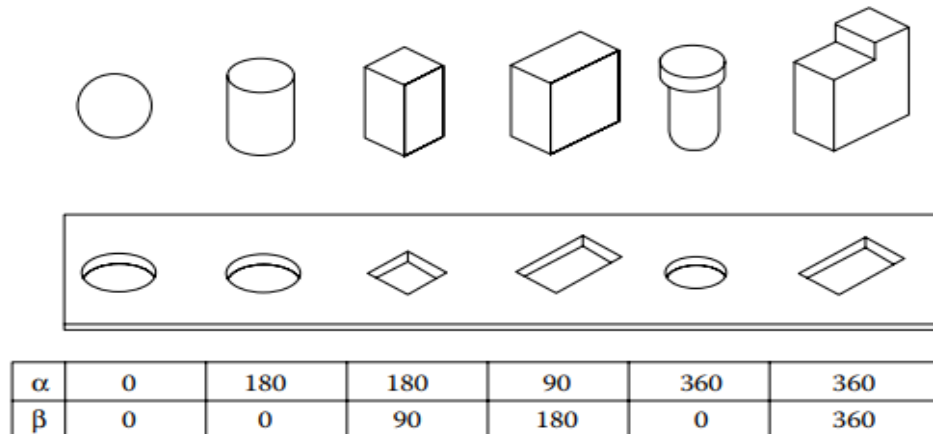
Simetría rotacional entre alfa y beta (Fuente: Design for manufacture and assembly)
